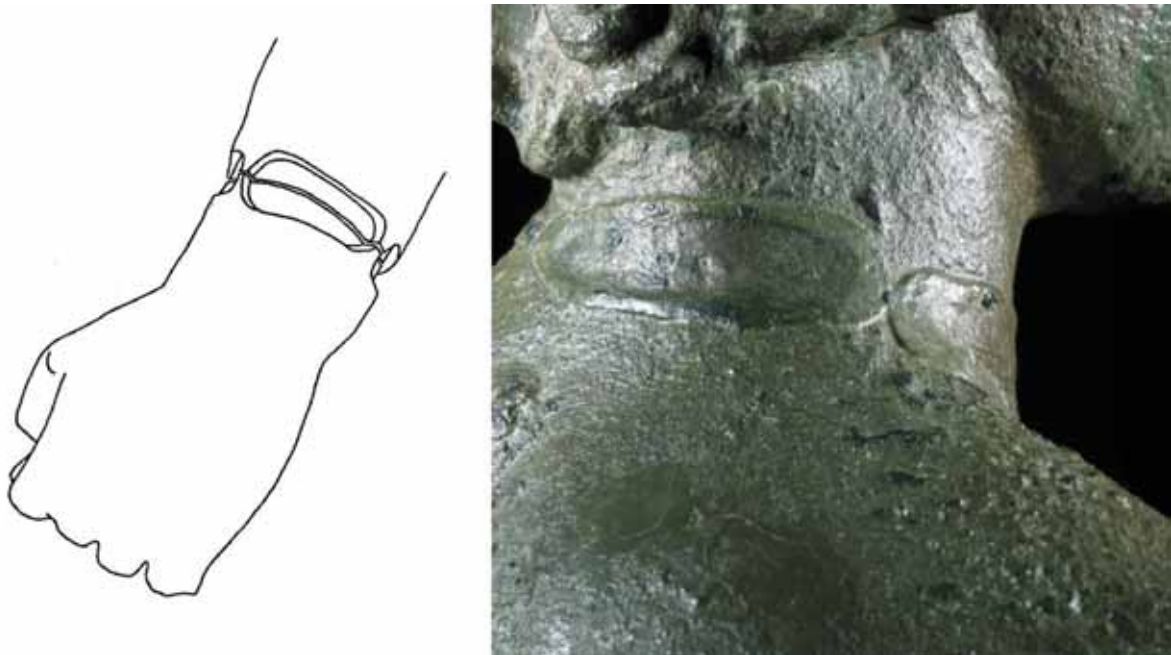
à gauche : reconstitution schématique de la préparation de la soudure en cuvettes de la main gauche de la statue A de Riace, ce type de cuvette est dit « non traversant » ; à droite : détail de la soudure en cuvettes de la tête de l'éphèbe d'Agde, h. 1,40 m, n°inv. 839, I<sup>er</sup> s. ap. J.C., musée d'Agde ; la corrosion différentielle des cuvettes explique qu'elles soient si facilement visibles.
